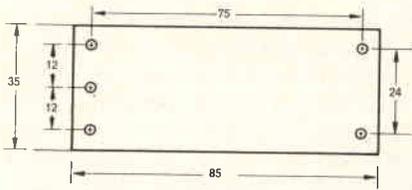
Dimensioni in millimetri e foratura principale della basetta isolante di supporto sulla quale devono essere fissati i componenti del circuito elettrico.
